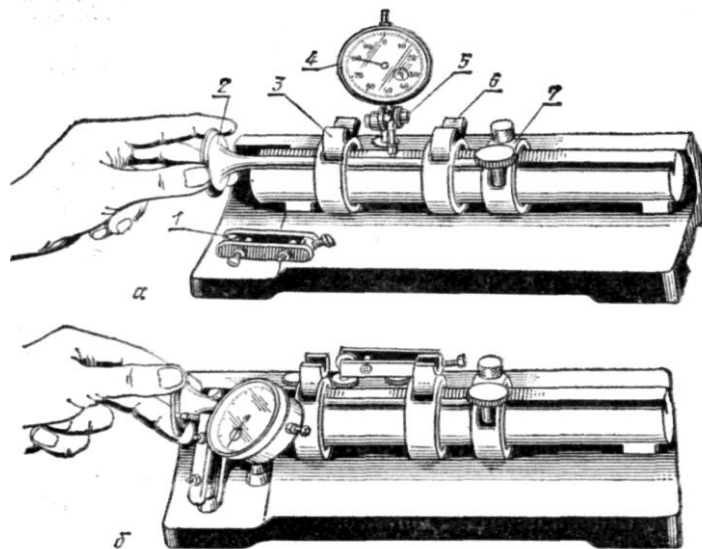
Проверка клапана на индикаторном приспособлении:
